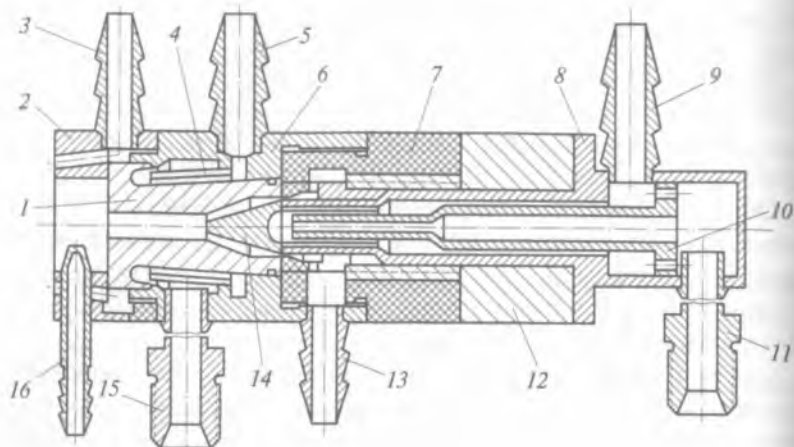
Схема плазматрона для напыления порошковых материалов: 1 — сопло; 2 — насадка; 3, 13 — штуцеры для ввода плазмообразующего газа; 4 — втулка; 5, 9 — штуцеры для подвода охлаждающей воды; 6 — корпус анода; 7 — изолятор; 8 — регулировочный сердечник; 10 — трубка; 11, 15 — штуцеры для отвода охлаждающей воды; 12 — корпус катода; 14 — вольфрамовый электрод; 16 — штуцер для ввода порошка в плазменную струю
